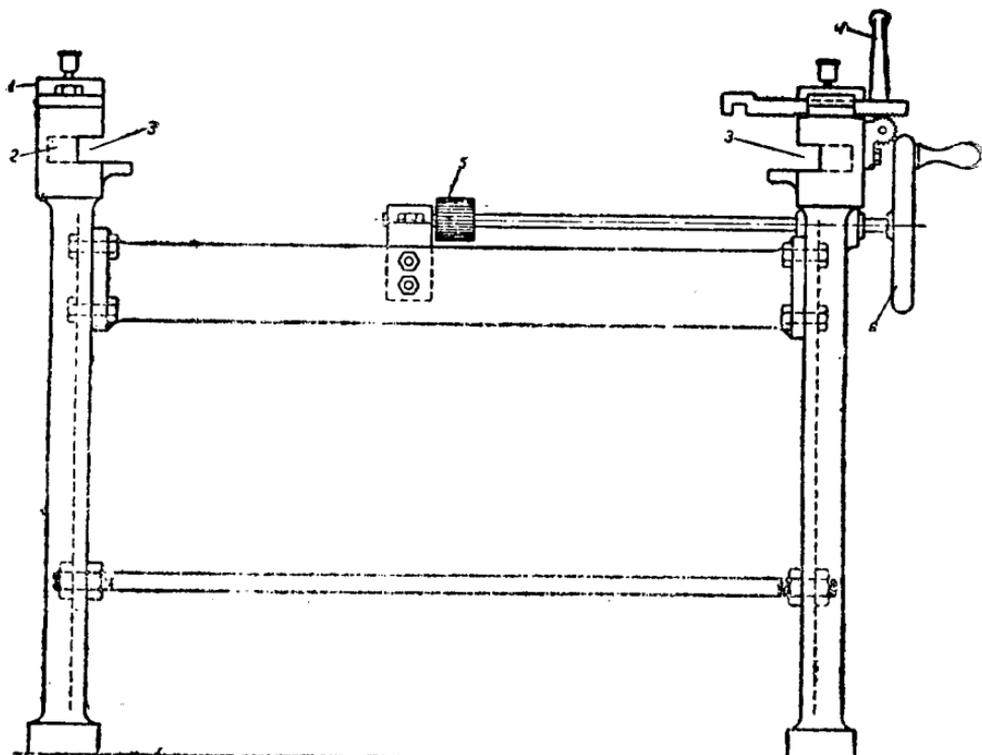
Проект ложкарного станка т. Пурецкого—вид спереди: 1—крышка под подшипника; 2—углубление в машине и кронштейн для поддержки приспособления с болванками при поперечном движении; 3—пазы, куда вставляется приспособление, с укрепленными в них плашками; 4—рукоятка и зубчатая рейка для поперечного движения приспособления с болванками; 5—шестерня, сцепляющаяся с зубчатыми рейками, находящимися под приспособлениями; 6—маховик для продольного движения приспособления.
